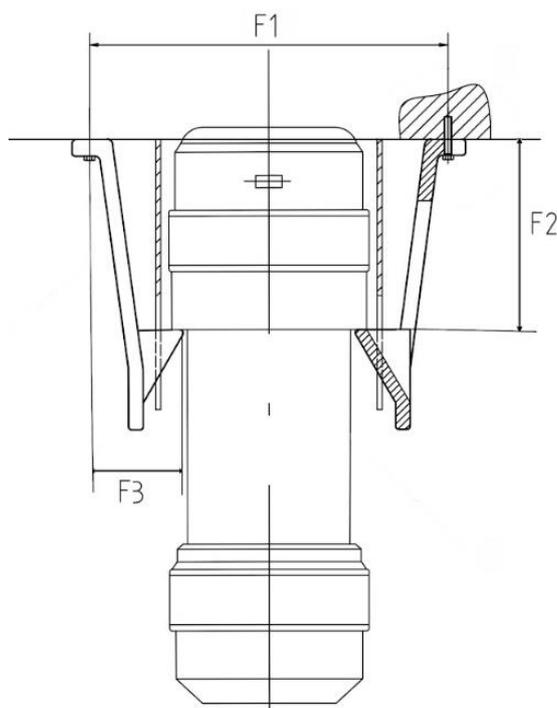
Marcado cotas sobre plano dimensionado previo.
